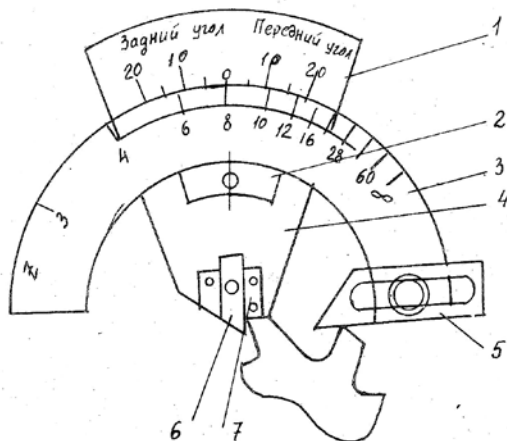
Измерение переднего и заднего углов развёртки прибором Бабчиницера
